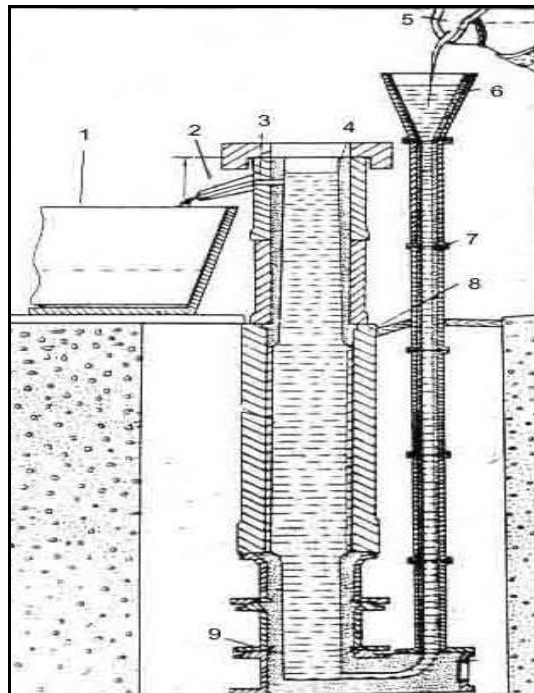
Схема литейной формы двухслойного валка: 1 – приемная мутьда; 2 – желоб; 3 – сливная летка; 4 – форма верхней шейки; 5 – ковш; 6 – воронка; 7 – стояк; 8 – кокиль; 9 – форма нижней шейки
